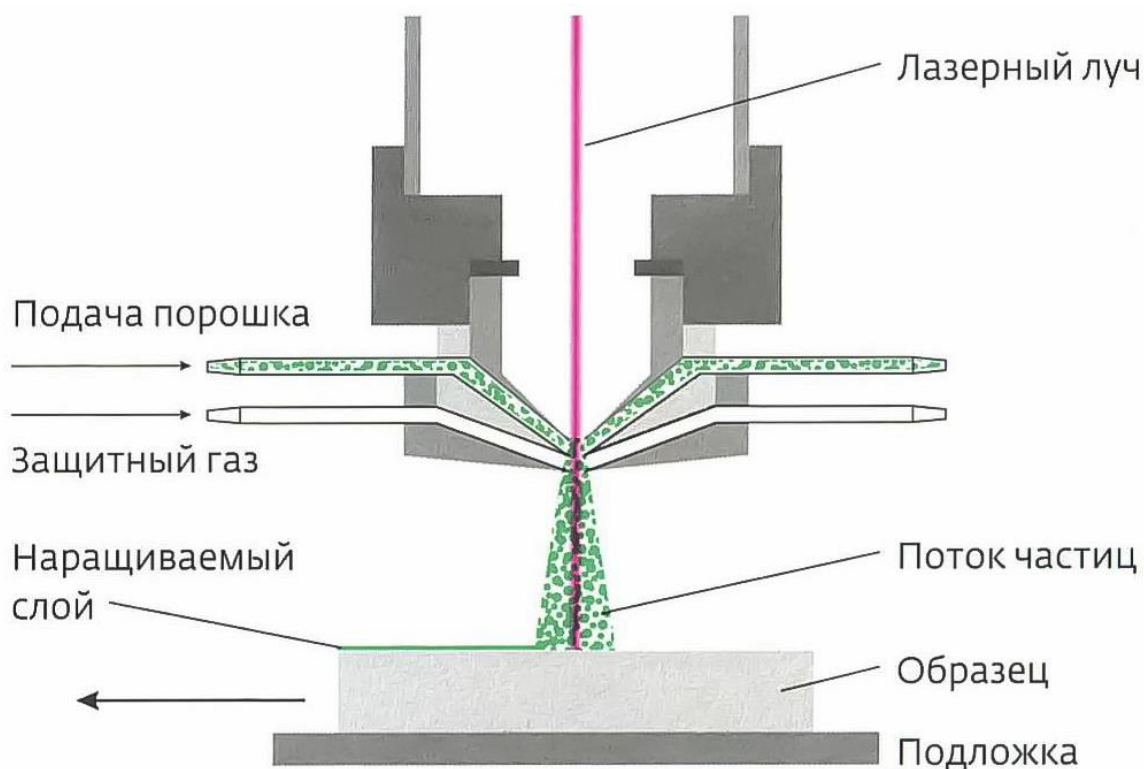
Схема послойной наплавки с подачей порошка, в среде защитного газа
